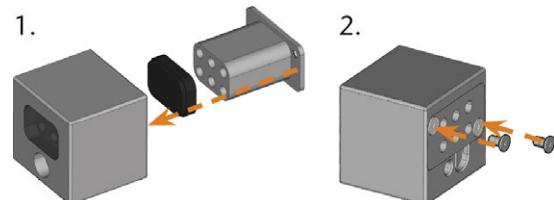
INSÉRER UN INSERT DANS UN MAGASIN D'OUTILS
